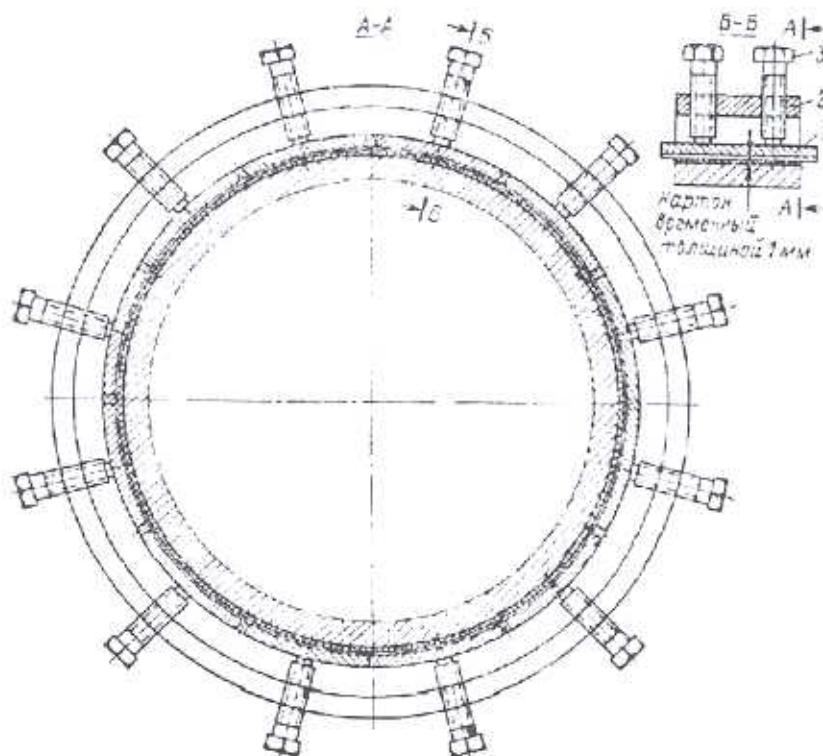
Сегментное приспособление для опрессовки изоляции контактных колец:
